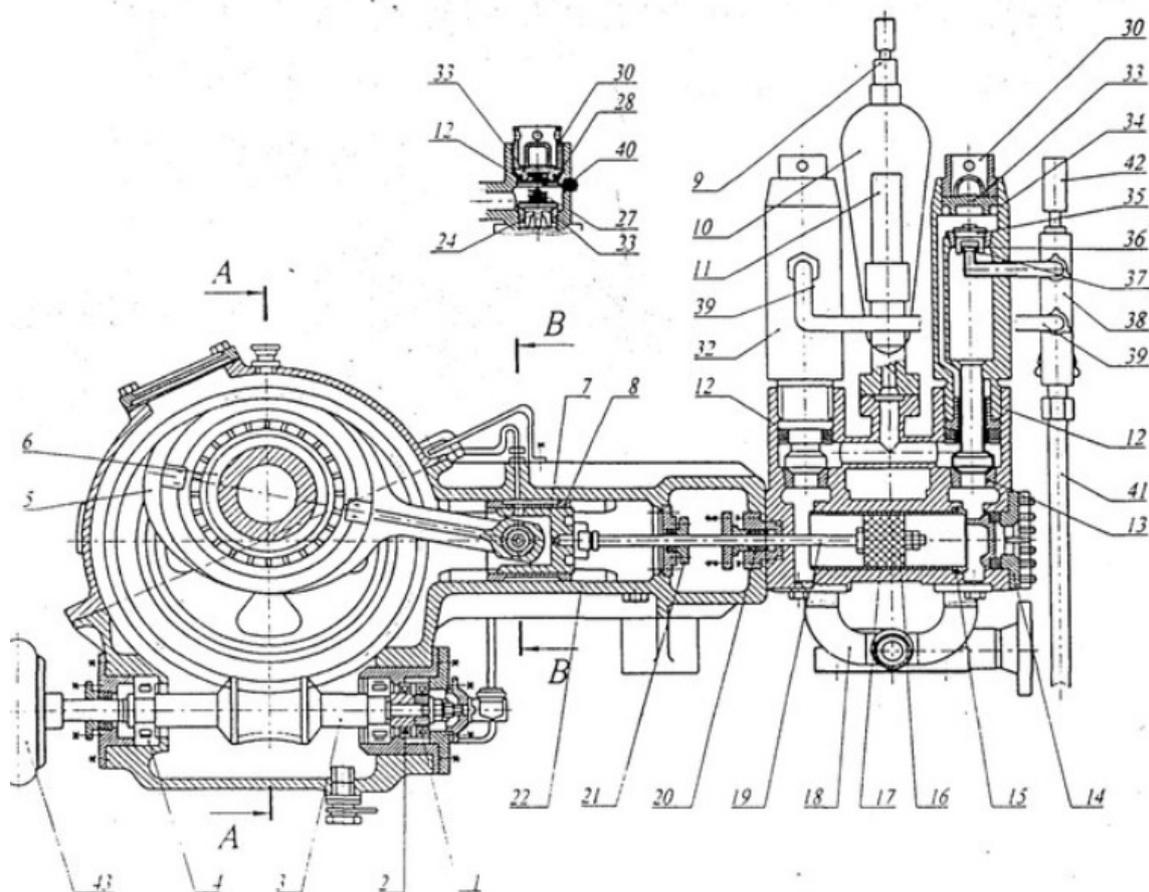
Насос газобустерный НПЦ-32: 1 – упорный шарикоподшипник 8320Л; 2 – упорный шарикоподшипник 8222; 3 – червяк; 4 – роликподшипник 32617М; 5 – шатун; 6 – пружинное кольцо; 7 – крейцкопф; 8 – накладка крейцкопфа; 9 – разделитель; 10 – нагнетательный коллектор; 11 – предохранительный клапан; 12 – клапанная коробка; 13 – седло клапана КСК 5-6; 14 – нажимная коронка; 15 – резиновое кольцо; 16 – поршень; 17 – цилиндрическая втулка; 18 – всасывающий коллектор; 19 – шток; 20 – сальник гидравлической части; 21 – сальник крейцкопфной камеры; 22 – станина; 23 – седло клапана; 24 – всасывающий клапан; 27 – пружина; 28 – манжета; 30 – гайка крышки; 32 – компрессионная камера; 33 – крышка клапана; 34 – корпус; 35 – клапан КСК 5-6; 36 – газовый клапан; 37 – гнездо; 38 – коллектор; 39 – газод; 40 – клапан дренажный; 41 – газопровод; 42 – манометр; 43 – муфта РКО
